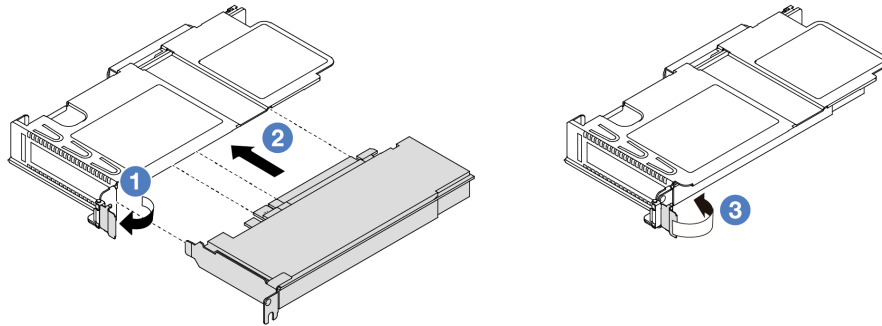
Instalação do adaptador PCIe no conjunto de placa riser LP-FH frontal
